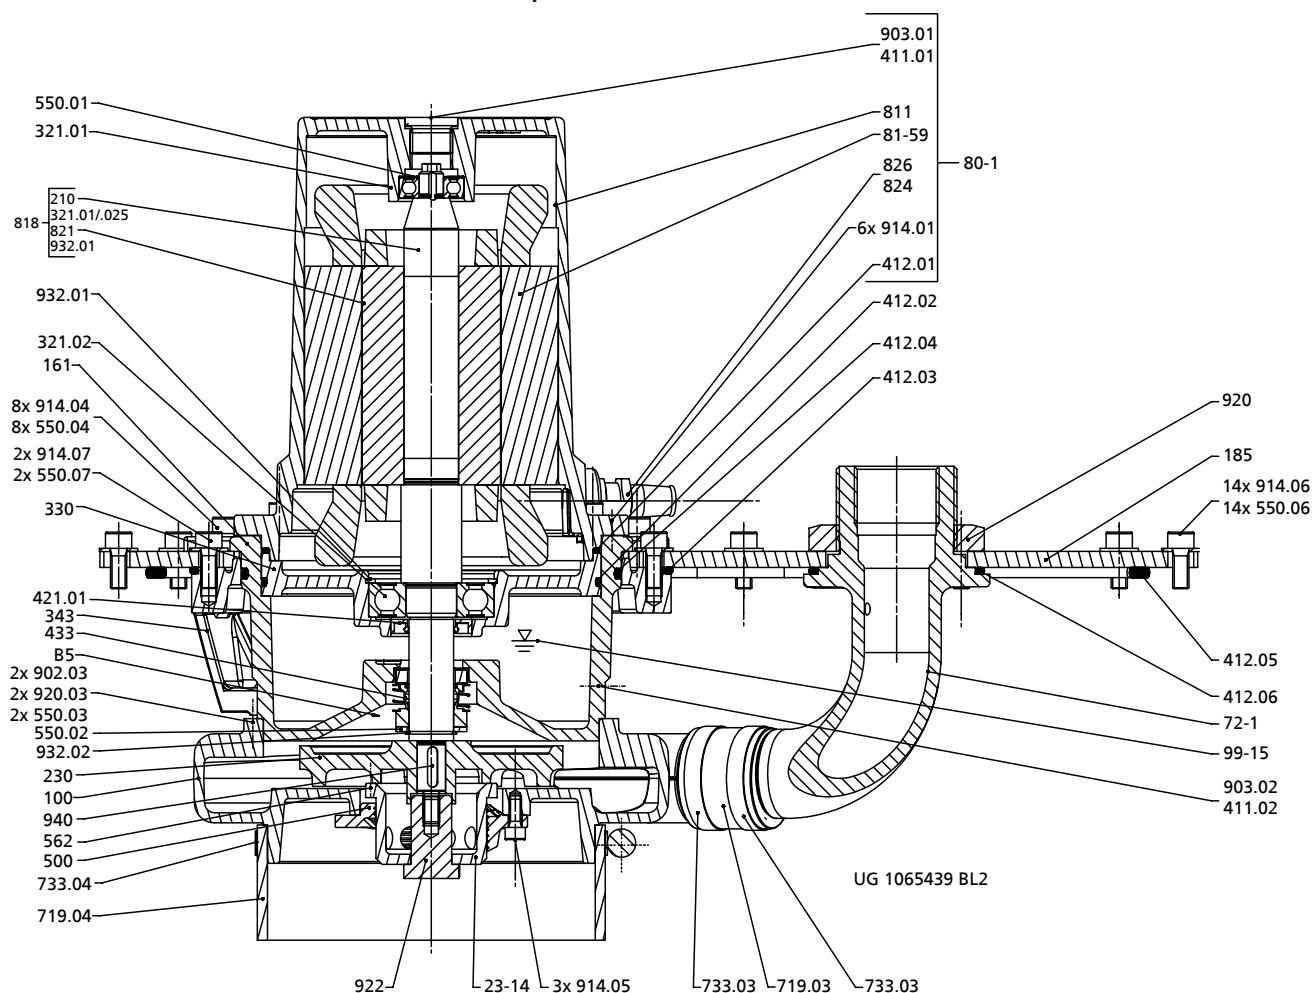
Gesamtzeichnung US100, UZS150 - Laufteil
